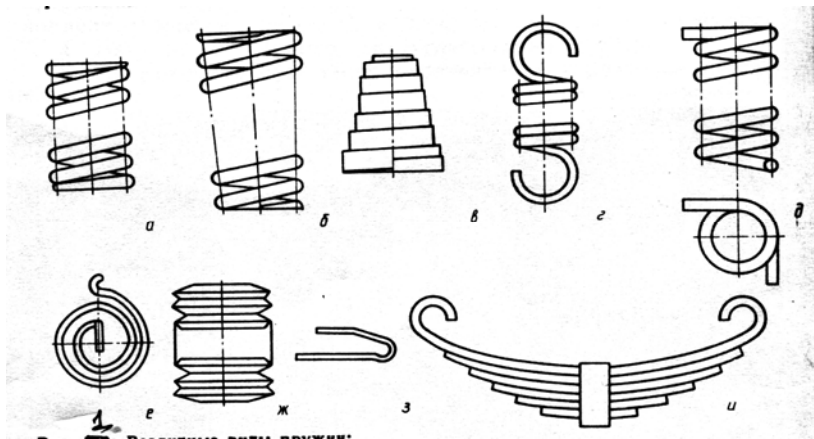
Різні види пружин: а – пружина стиснення циліндрова; б – пружина стиснення конічна з дроту круглого перетину; в – пружина стиснення телескопічна із заготовки прямокутного перетину; г – пружина розтягування циліндрова; д – пружина кручення; е – пружина спіральна плоска; ж – пакет тарілчастих пружин; з – пружина вигину пластинчаста; і – листова ресора
